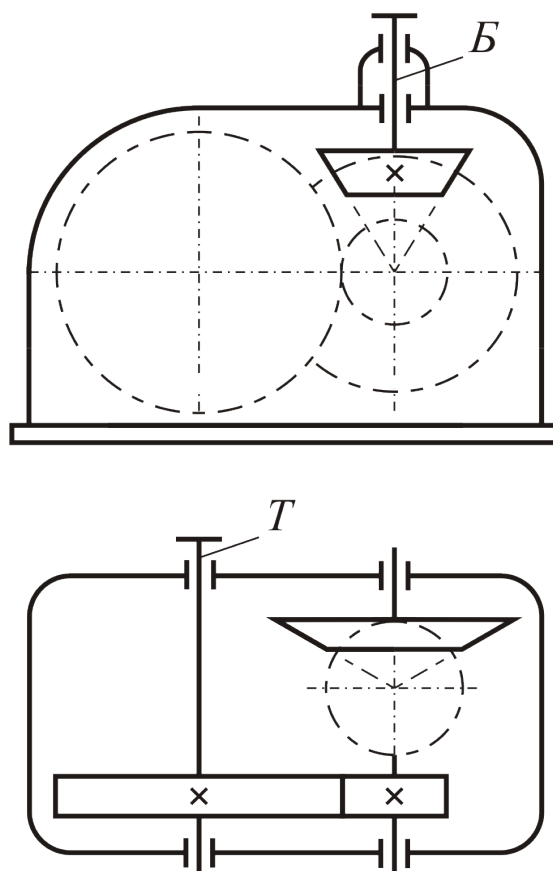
Кинематическая схема двухступенчатого коническо-цилиндрического редуктора с вертикальным быстроходным валом
